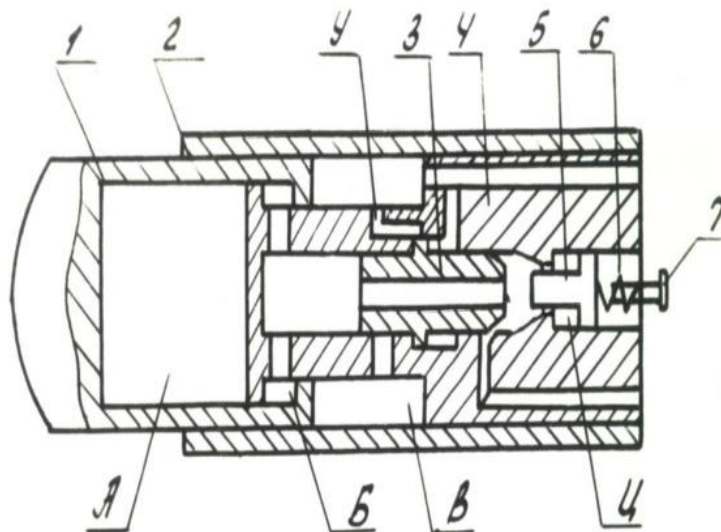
Конструктивная схема гидравлического ударника с одноступенчатым органом управления: 1 – боек; 2 – корпус; 3 – золотник; 5 – поршень; 6 – упругий элемент; 7 – регулировочный винт; Ц – цилиндр; А,Б,В,У – камеры соответственно: пневматическая; обратного хода; вспомогательная; управления
